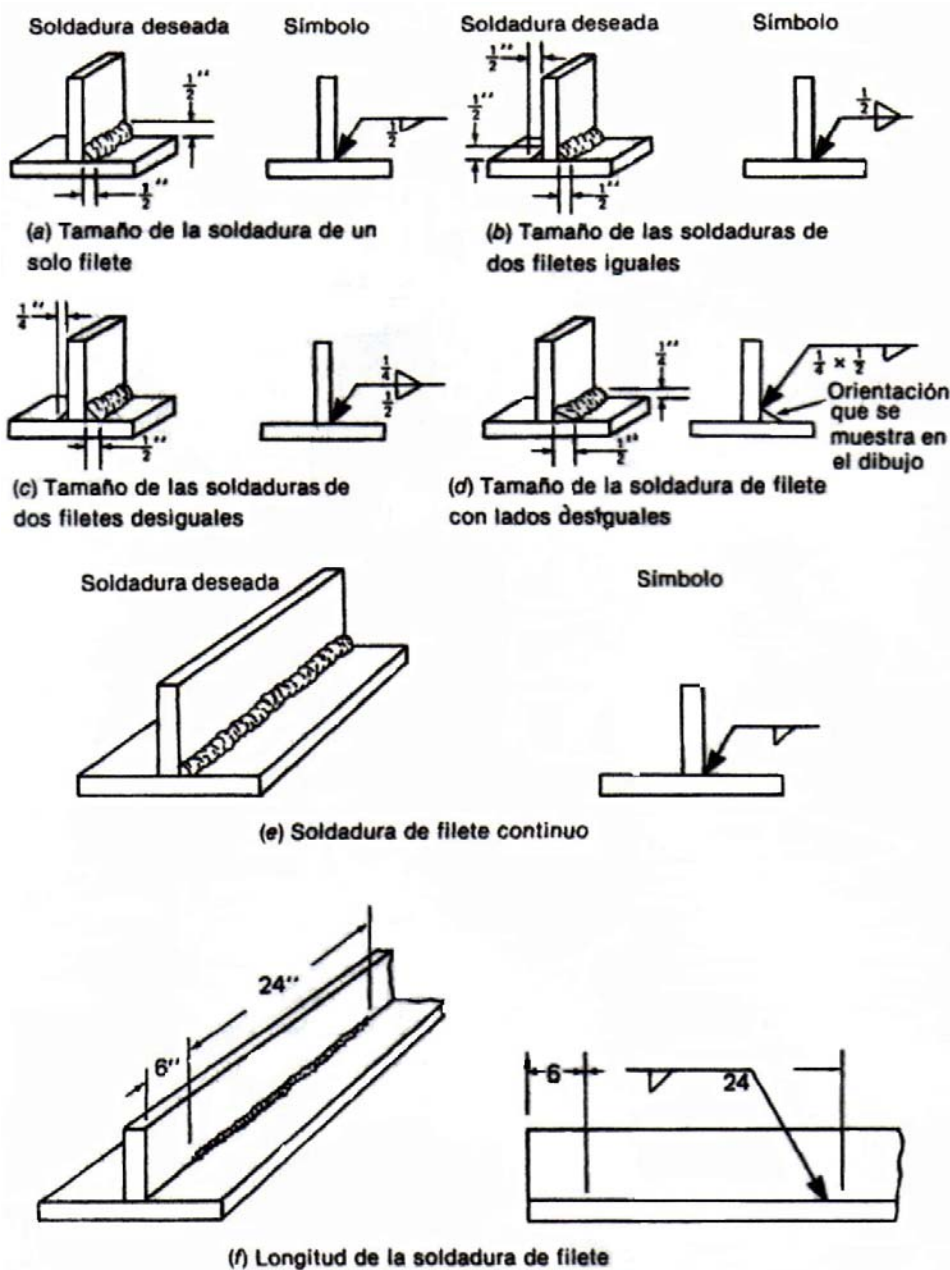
Algunos símbolos de soldadura y las soldaduras representadas por ellos.
